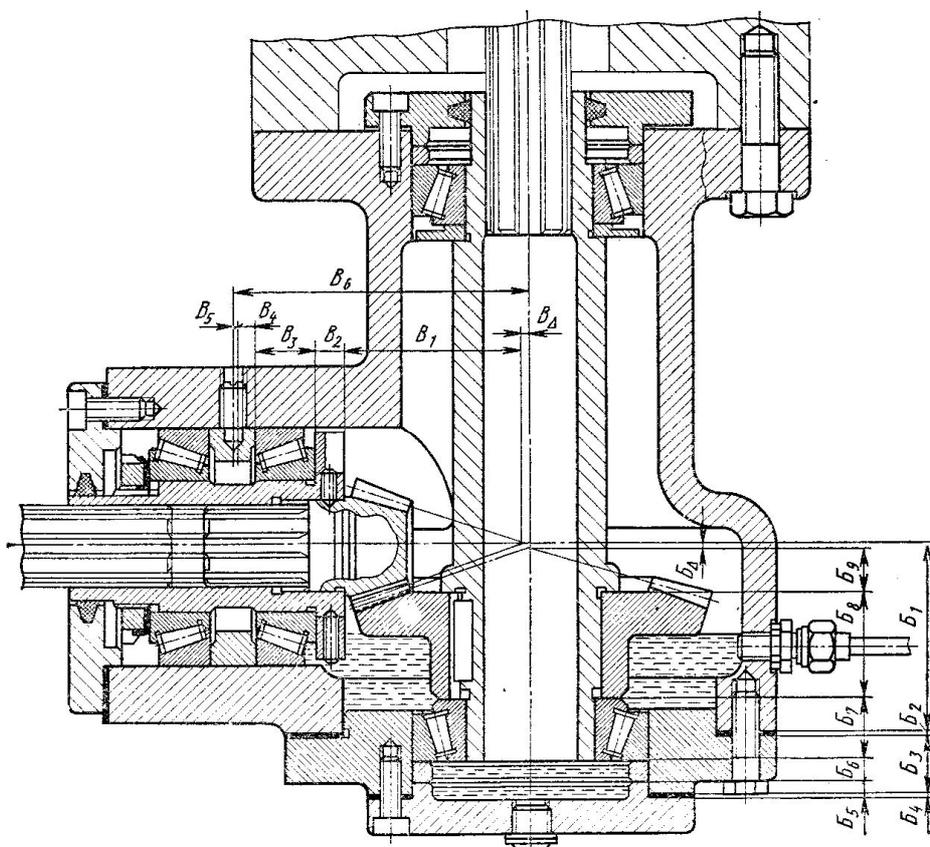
Схемы размерных цепей, определяющих точность совпадения вершин делительных конусов конических зубчатых колес
